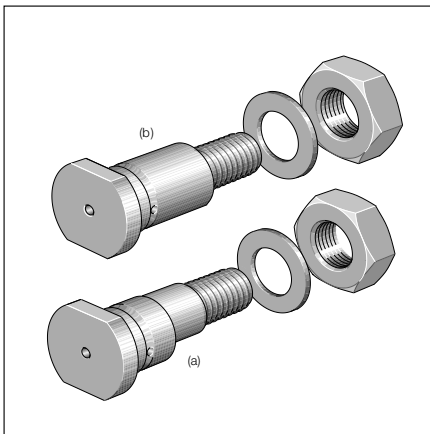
Befestigungs-Zapfen für Profillaufrollen
